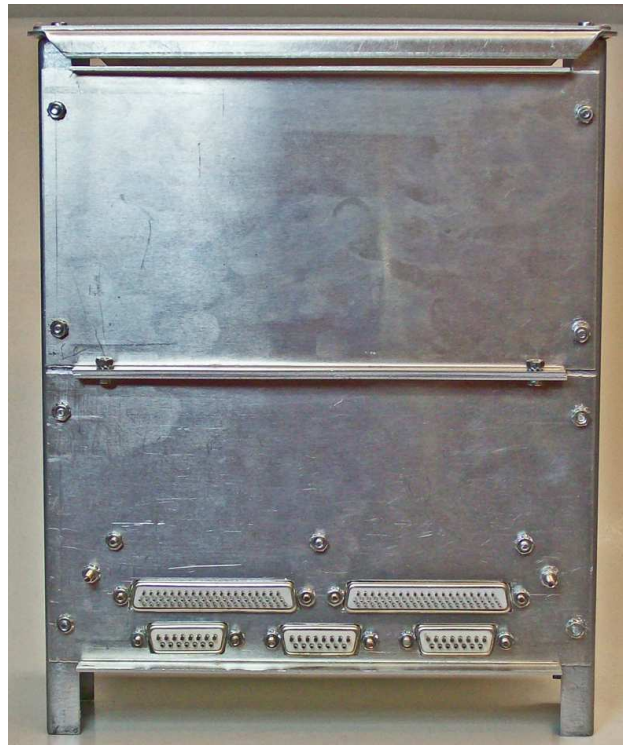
Montageblech 1 mit Buchsen für die Frontplatte und den Steuerrechner
